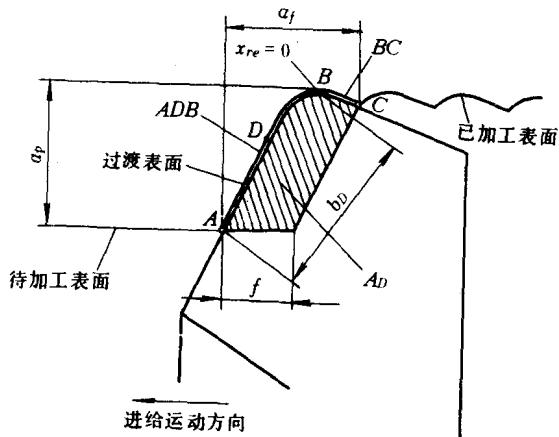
车削时的吃刀量、进给量及切削层尺寸
